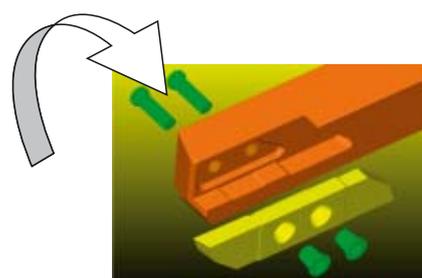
Le due boccole inseribili si montano e si smontano facilmente in una plachetta standard e sono riutilizzabili.
